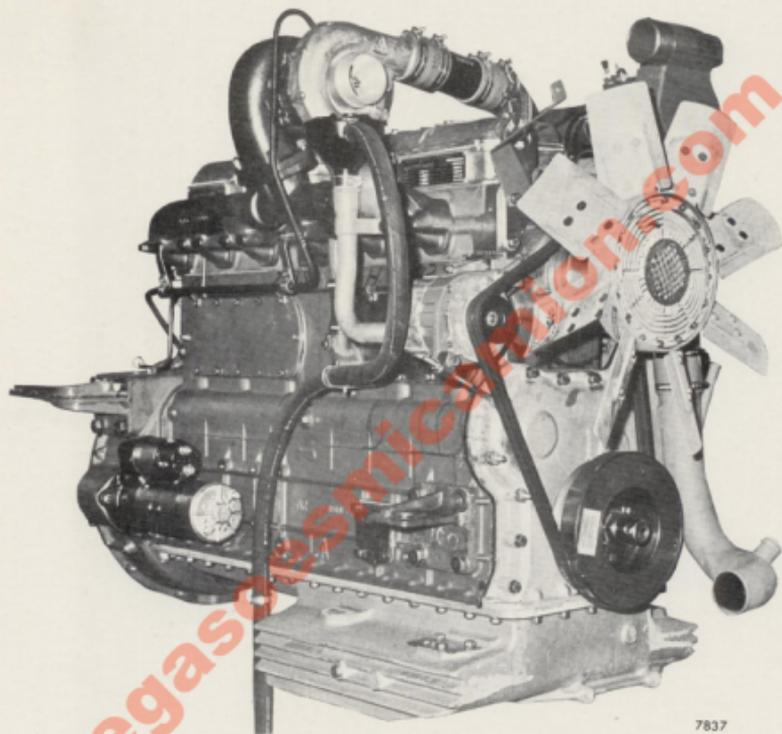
Motor 9156, lado derecho (Montaje DESDE)
